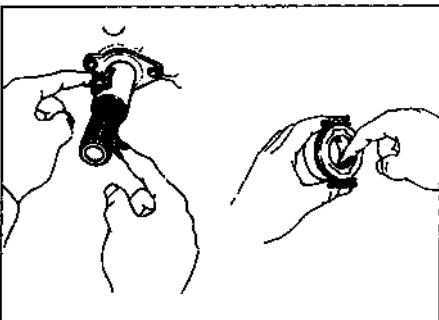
Нанесите немного тугоплавкой смазки на внутреннюю поверхность подшипника, шлицы и горловину первичного вала коробки передач
